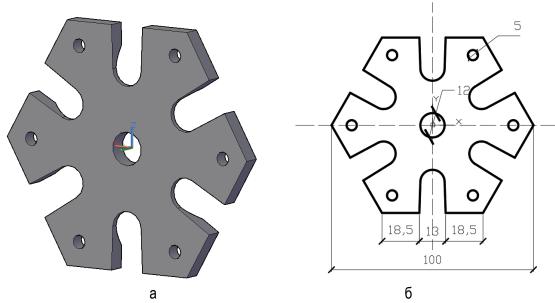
а – 3-D модель пластины; б – двухмерный чертеж пластины
